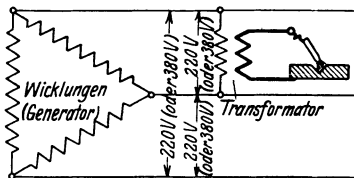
Drehstromsystem in Dreieckschaltung mit Schweißtransformator zwischen zwei Phasen.
